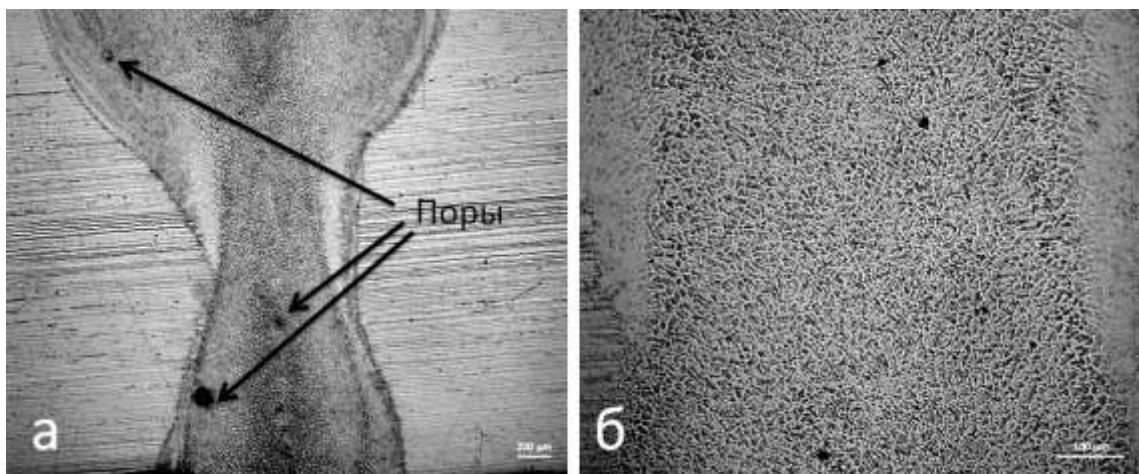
Сварной шов, полученный лазерной сваркой
